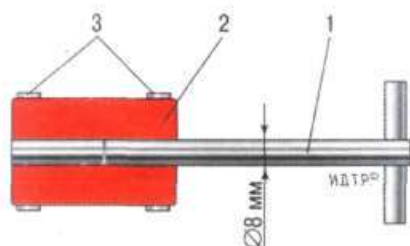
Приспособление для притирки клапанов: 1 – металлический стержень; 2 – резиновый шланг; 3 – винтовой хомут
